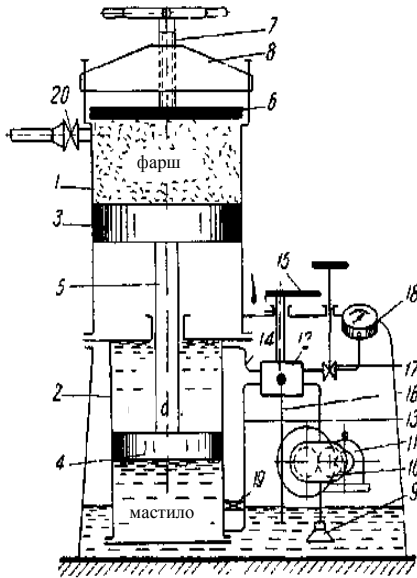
Схема гідравлічного шприца періодичної дії: 1 – фаршевий циліндр; 2 – силовий циліндр; 3, 4 – поршні; 5 – шток; 6 – відкидна кришка; 7 – шпindelь; 8 – траверса; 9 – прийомна сітка; 10 – шестерний насос; 11 – електродвигун; 12 – розподільний кран; 13 – труба; 15 – рукоятка; 16 – зливальна трубка; 17 – запобіжний пружинний клапан; 18 – манометр; 19 – запобіжний клапан; 20 – кран
